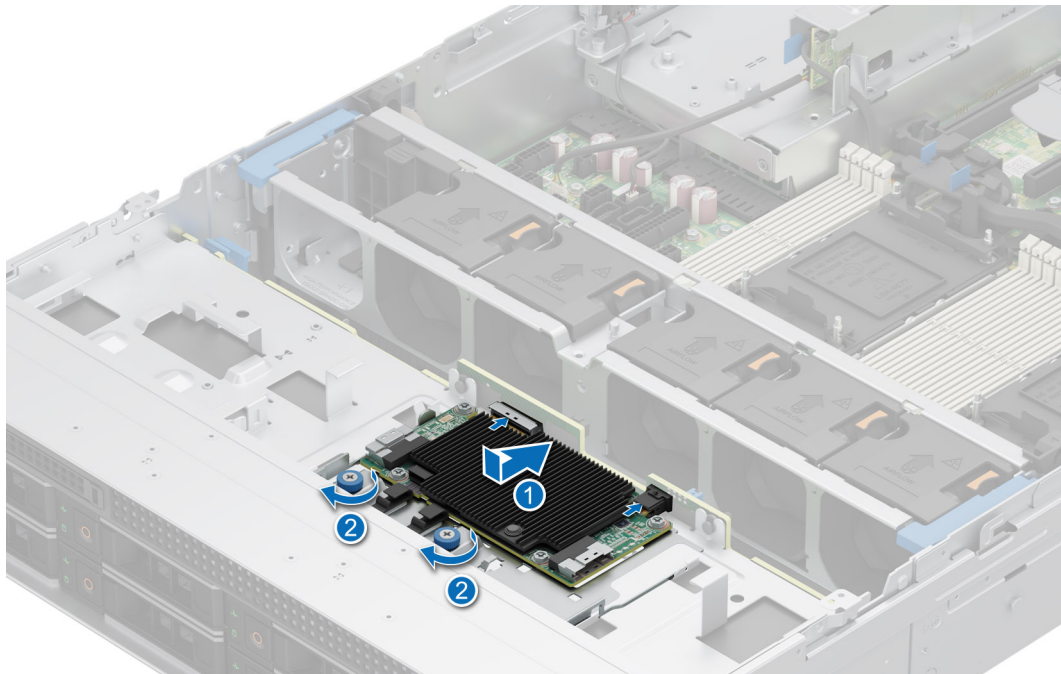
Instalación del módulo de PERC frontal de montaje frontal
